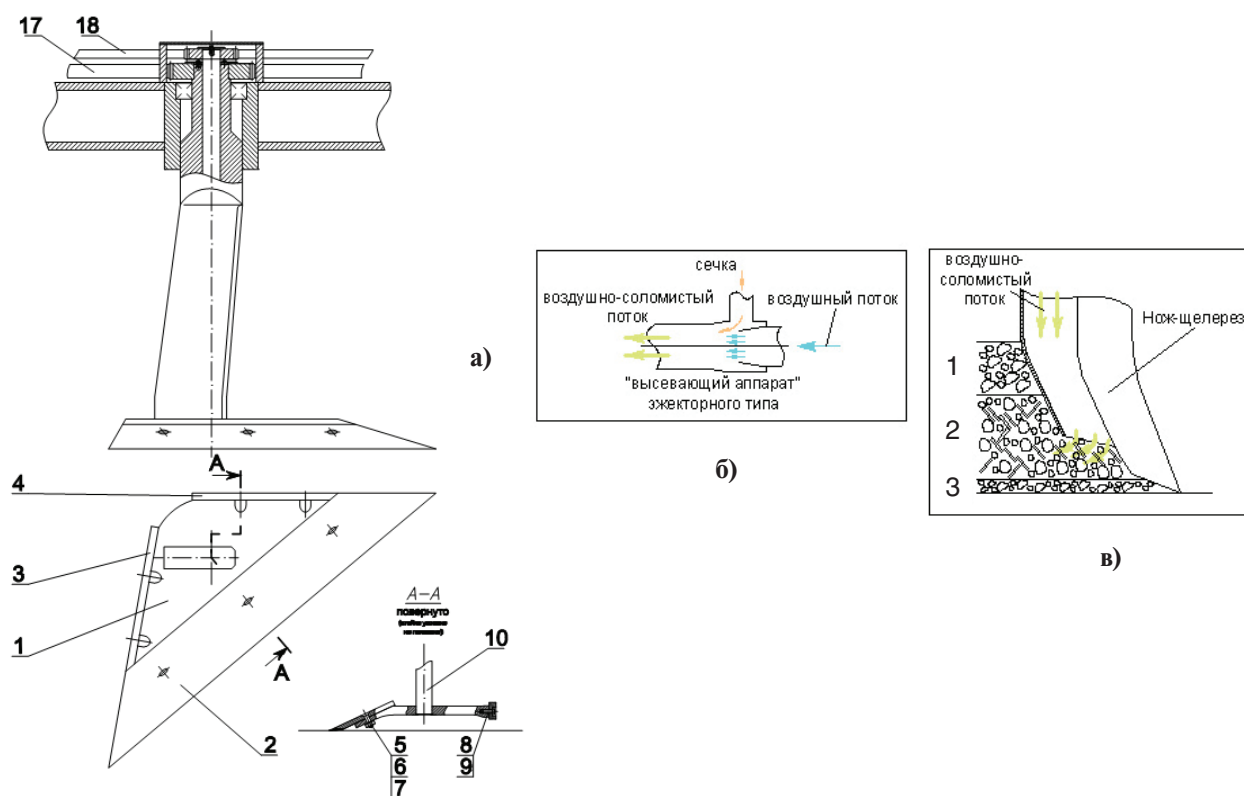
Общее устройство плужного рыхлителя с поворотными корпусами для гладкой вспашки:
